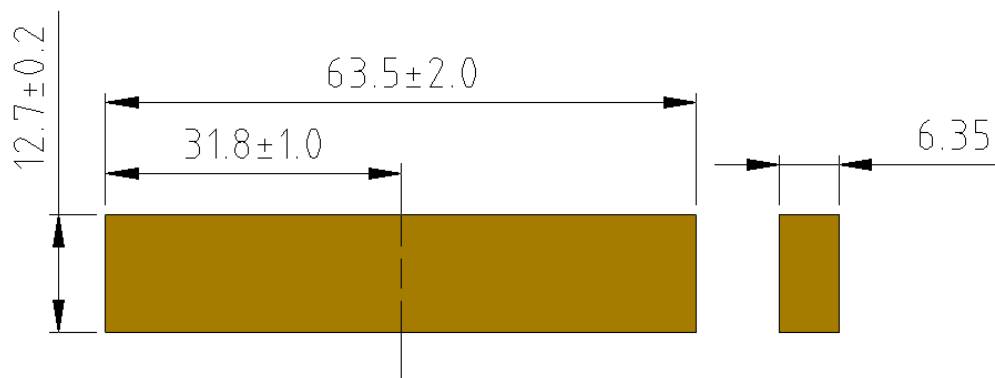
Dimensiones de probetas tipo E para ensayo de impacto según la norma ASTM D256-10.
